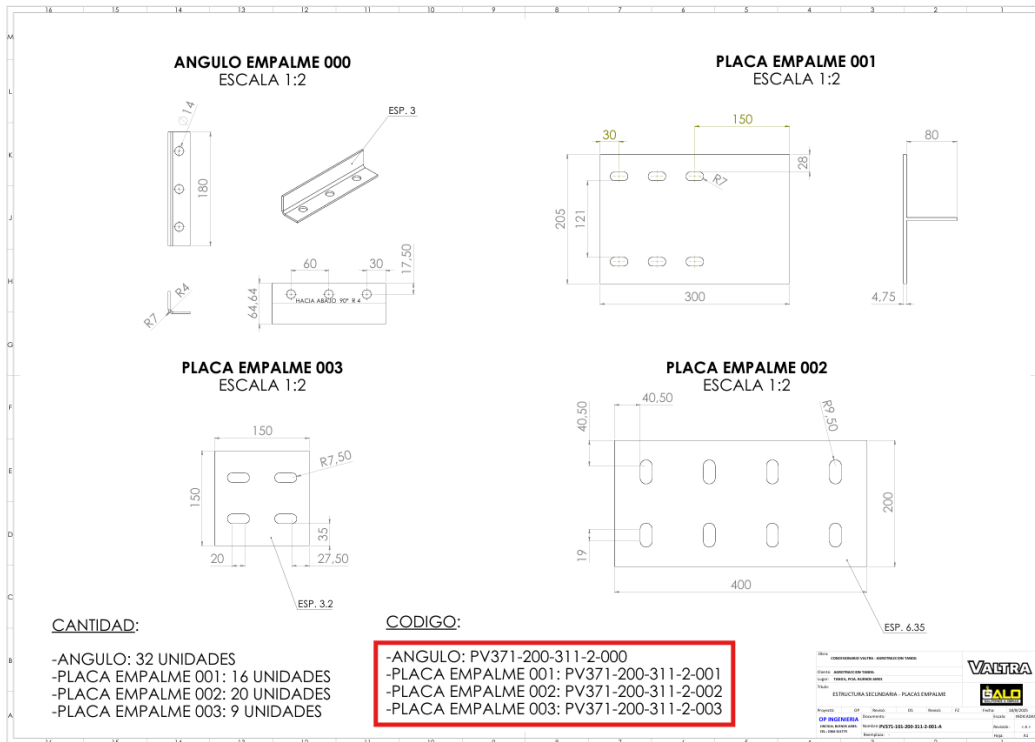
Plano de corte. Fuente: Elaboración propia.
